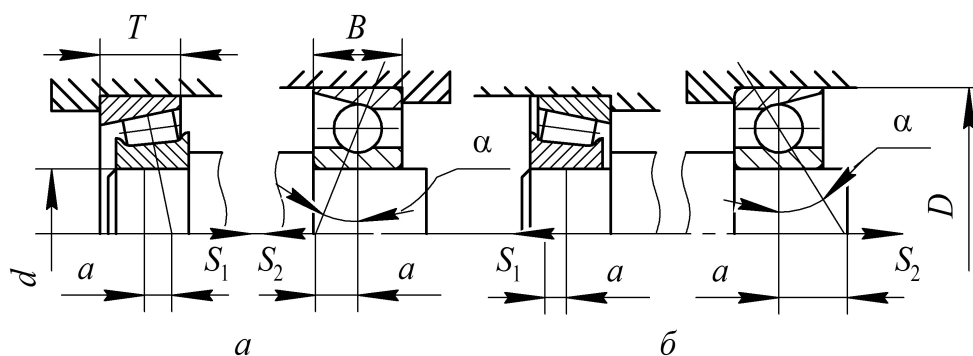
Схемы установки радиально-упорных подшипников на валах:
